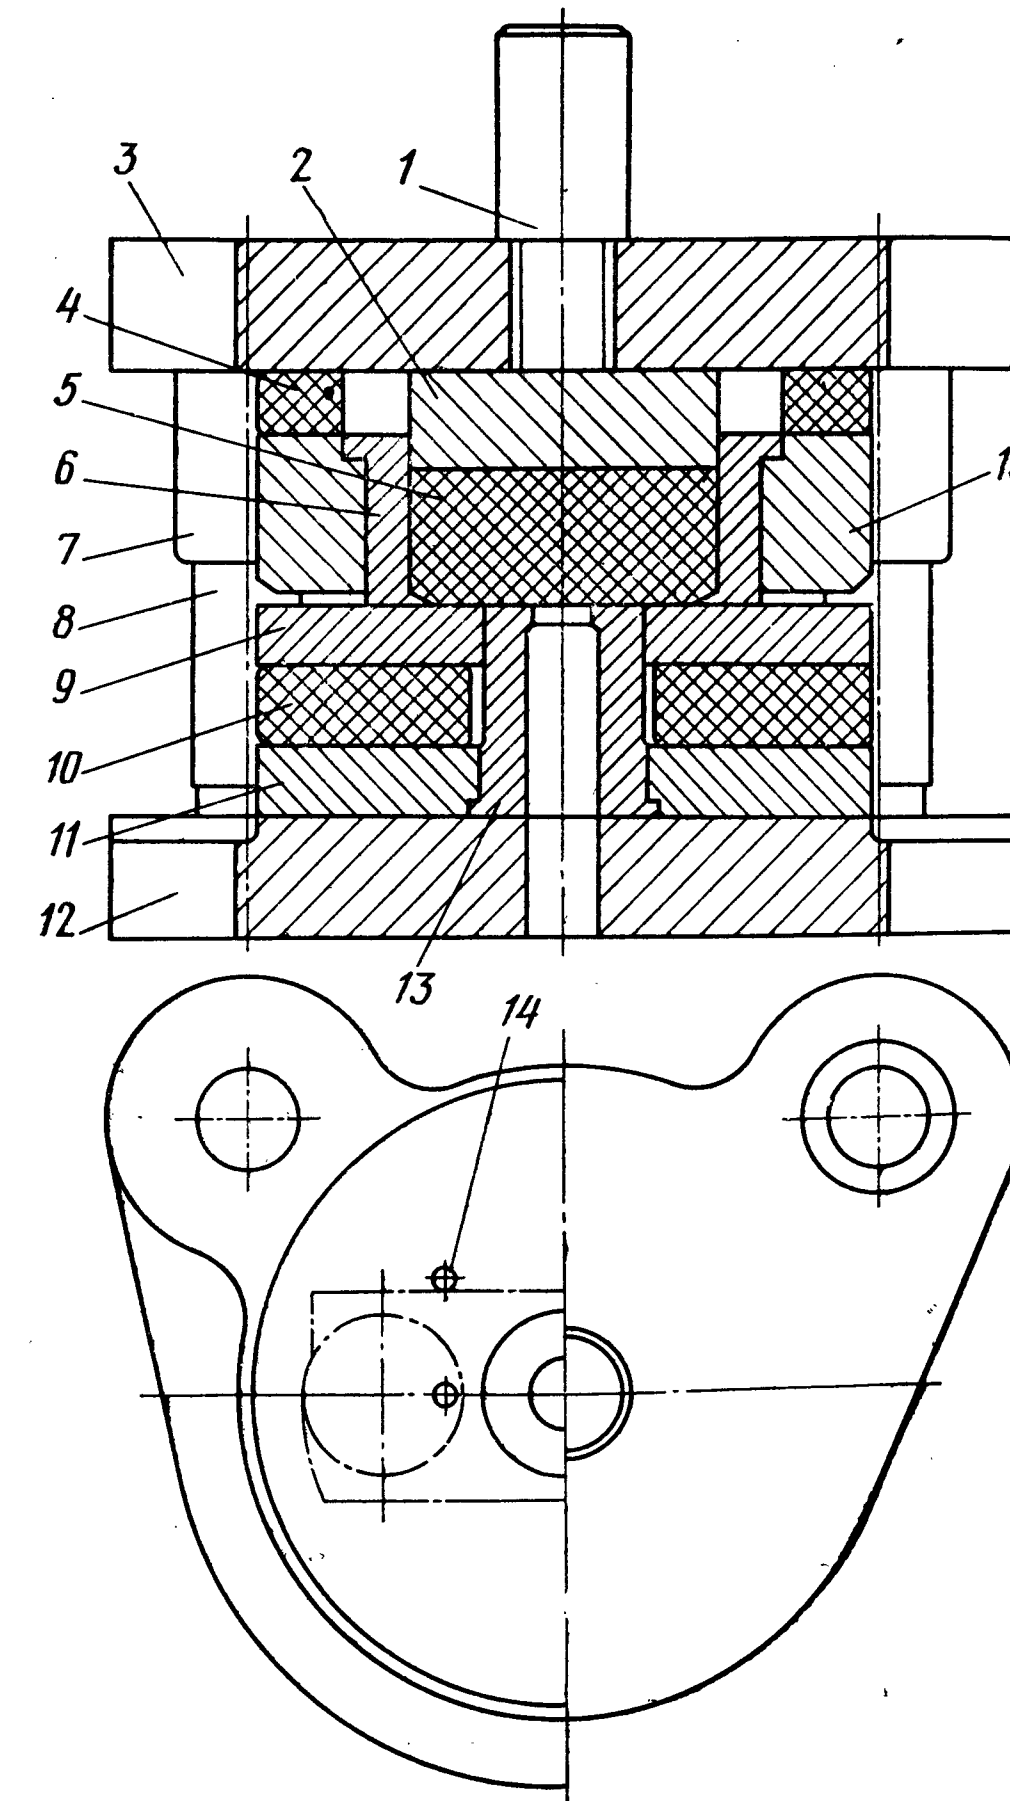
Штамп с полиуретановой матрицей для вырубки шайбы
